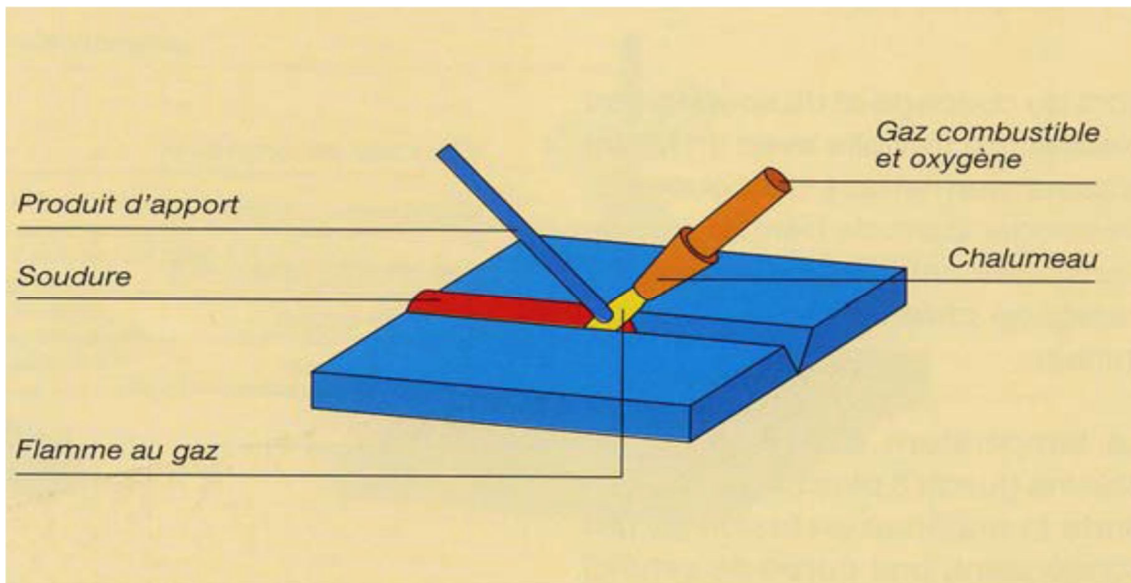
Principe du soudage oxygaz. [16]
